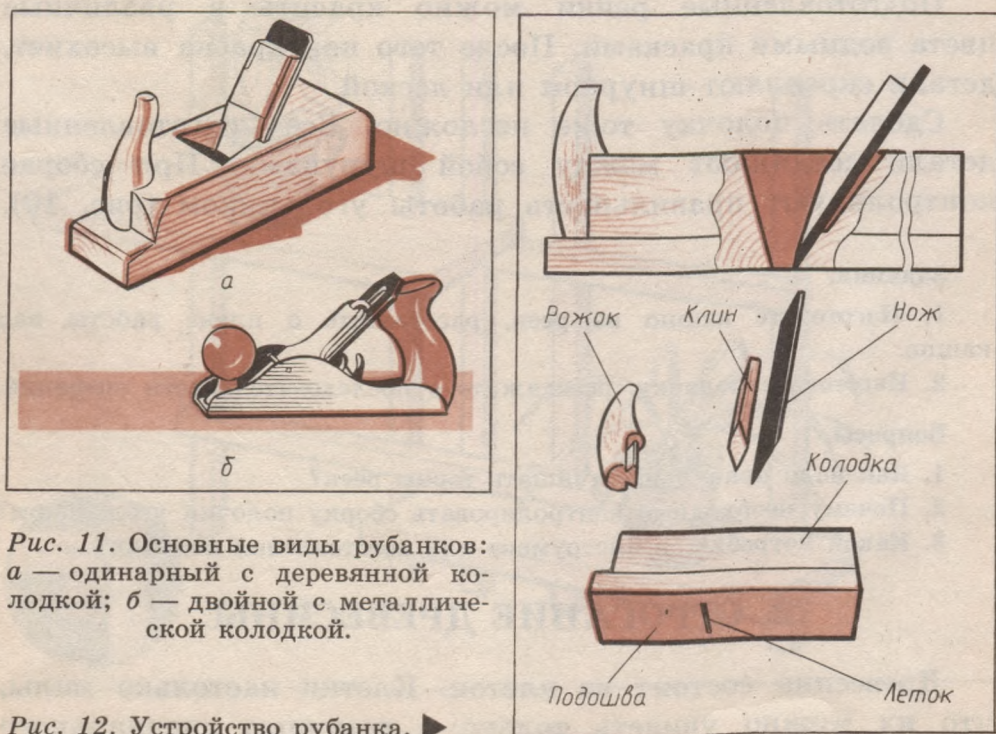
Основные виды рубанков: а — одинарный с деревянной колодкой; б — двойной с металлической колодкой.
